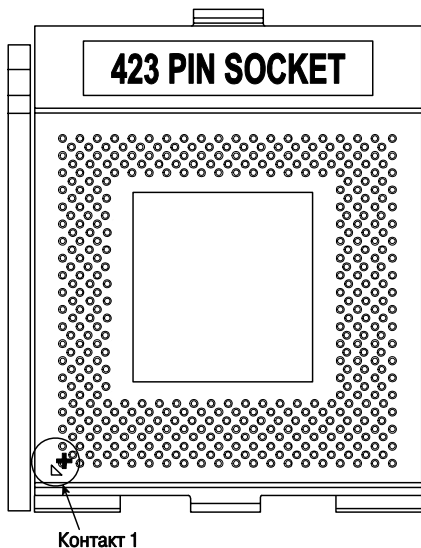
Расположение вывода 1 гнезда Socket 423 (Pentium 4)
